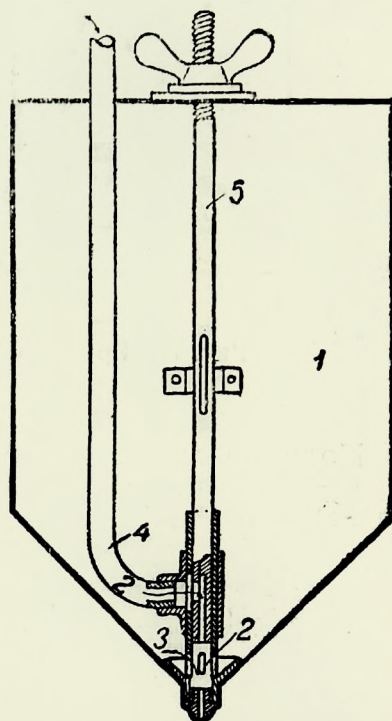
Схема пескоструйного аппарата для сверления дыр
